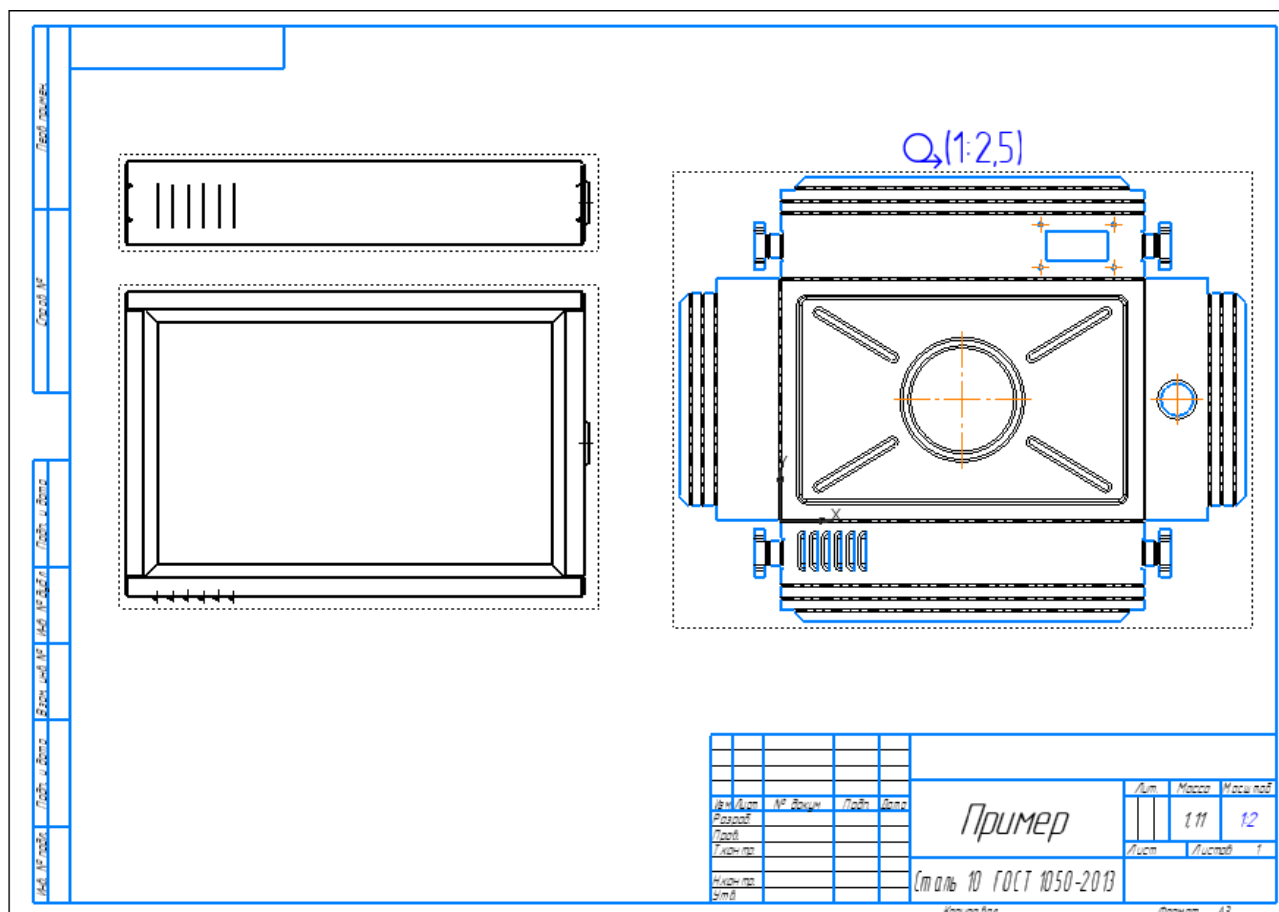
Пример чертежа детали «Корпус» с разверткой
